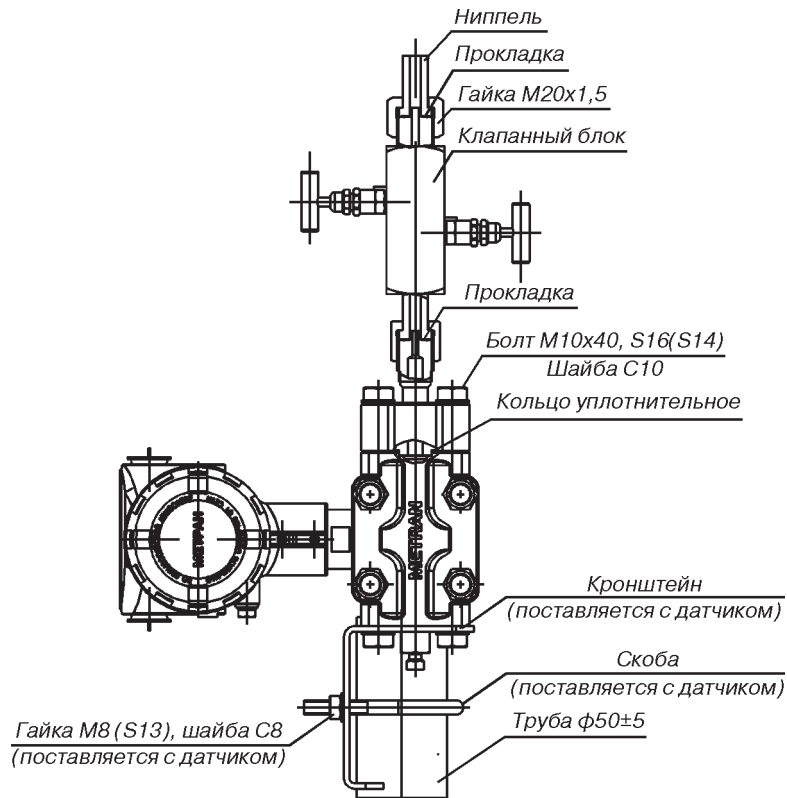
Пример монтажа датчика давления Метран-150CG с установленным клапанным блоком 0106 М Т 2 и кронштейном для датчика давления. Габаритные и присоединительные размеры см.рис.21.
